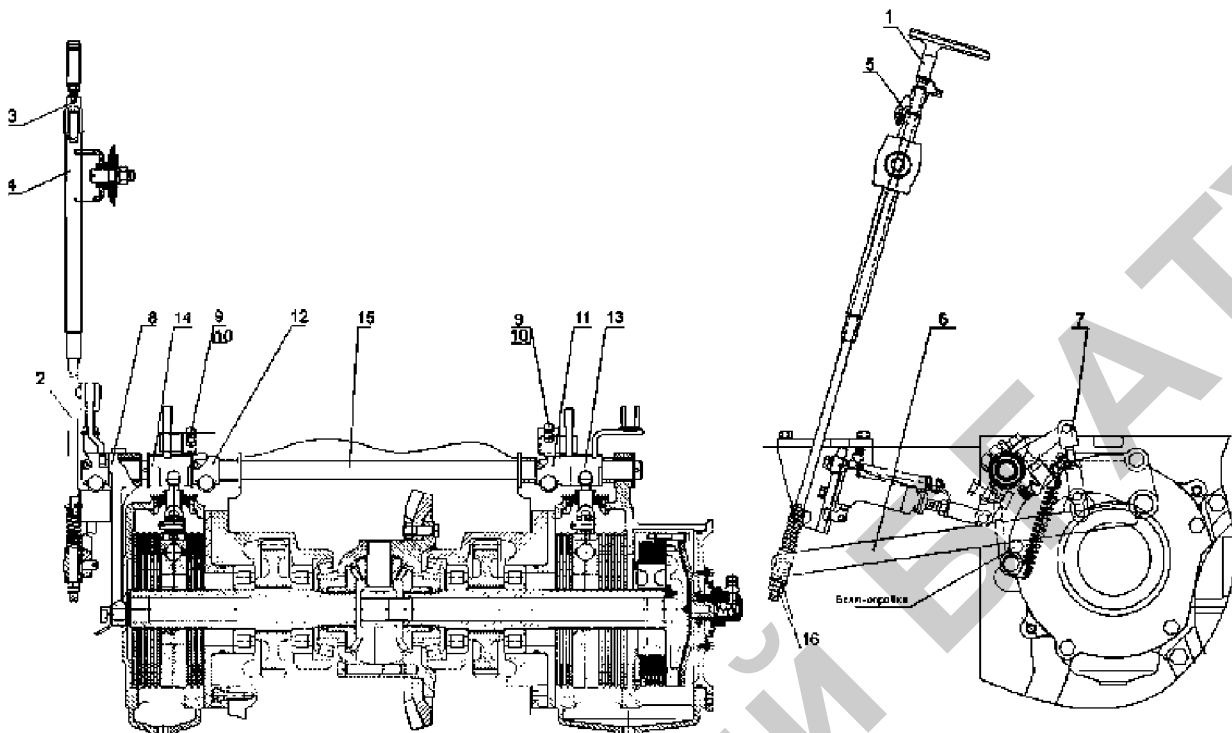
Привод стояночного тормоза трактора «БЕЛАРУС-1523»:
